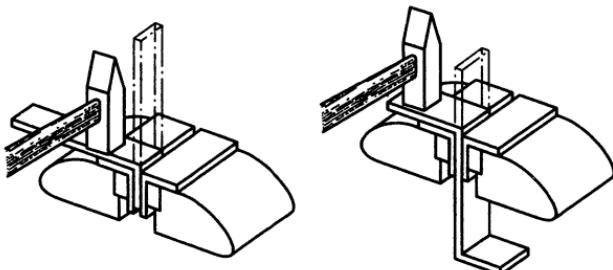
Гибка полосового металла в слесарных тисках под прямым углом
